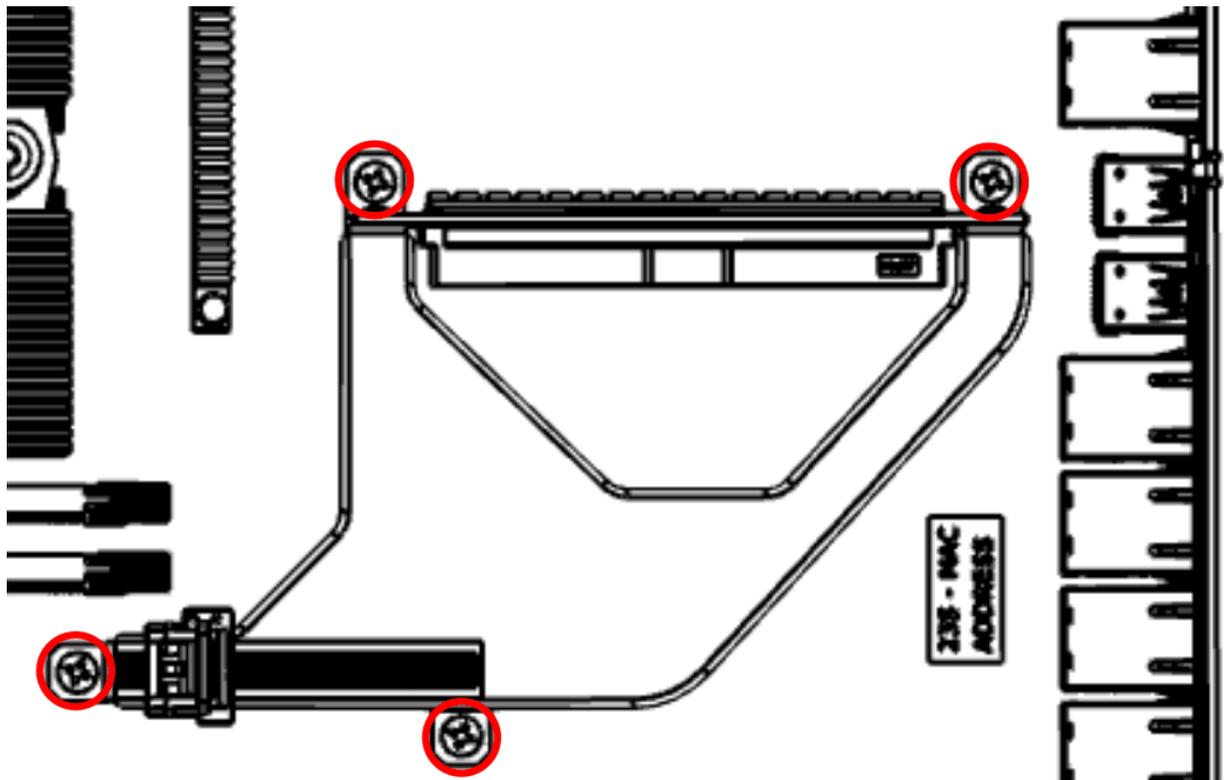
Schrauben der PCIe-Riserkarte wieder anbringen
